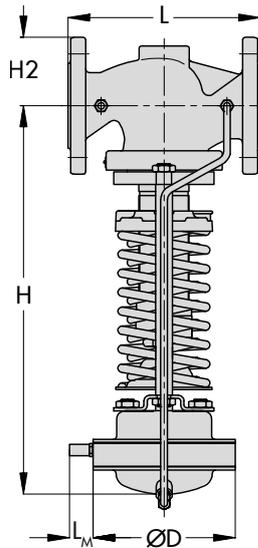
Abmessungen Sicherheitsabsperrentil mit eingebautem Druckminderer (SAV) Typ 36-4
